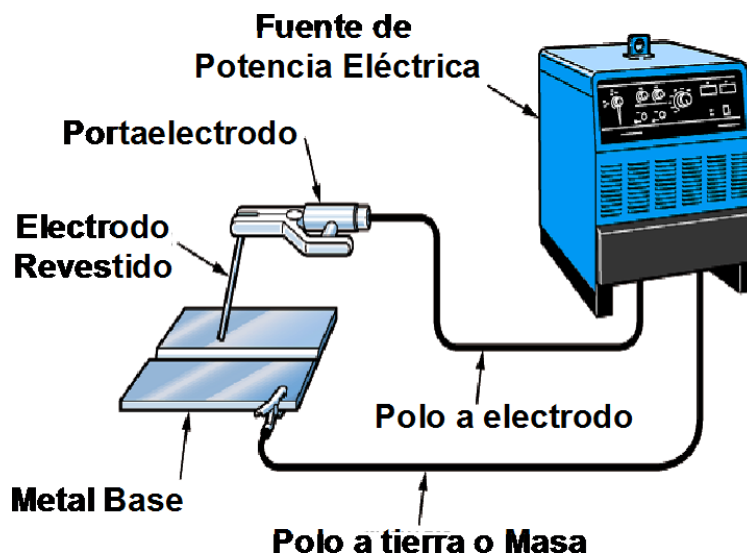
Equipo de Soldadura SMAW [7]
